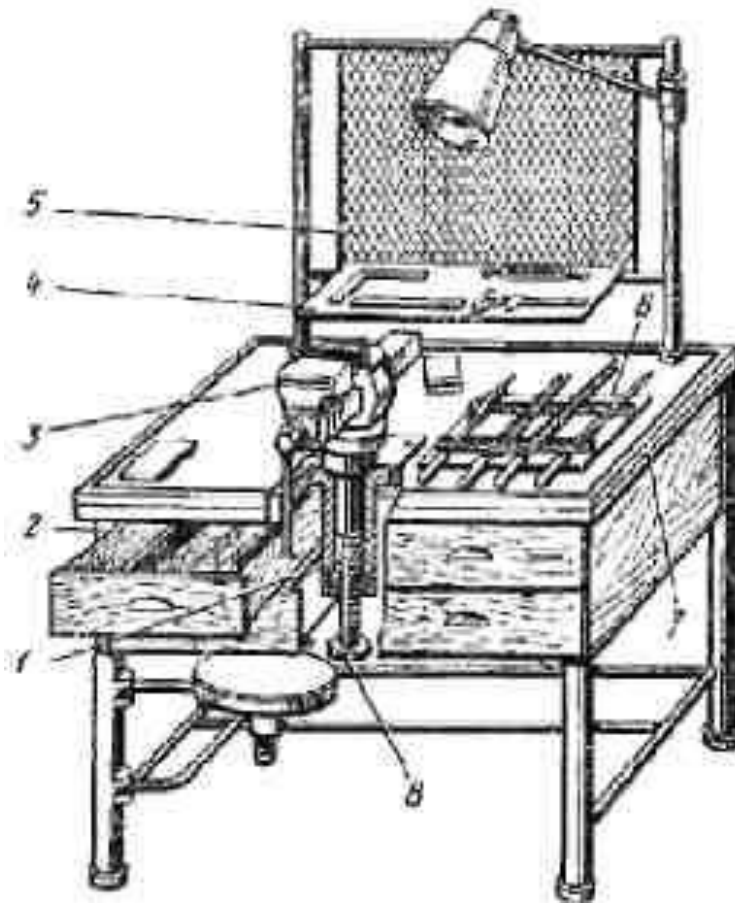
Слюсарний верстак: 1 – гвинт підйому; 2 – шухляда; 3 – лещата; 4 – поличка; 5 – сітка; 6 – планшет для інструментів; 7 – окантовка (бортик); 8 – гайка.
